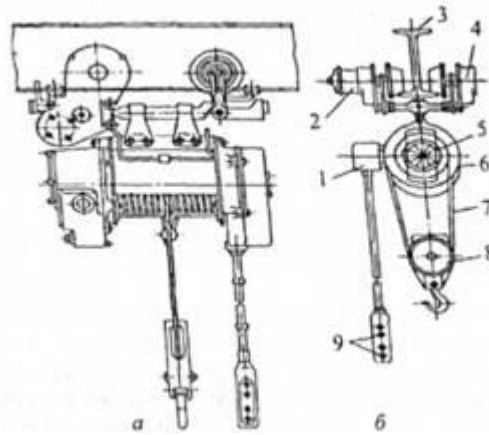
Електричний таль; а — зовнішній вигляд; б — схема: 1 — магнітний пускач; 2 — електродвигун для пересування; 3 — рейка; 4 — ходовий візок; 5 — електродвигун для підймання; 6 — корпус вантажного механізму; 7 — канат; 8 — підвіска; 9 — кнопки керування
